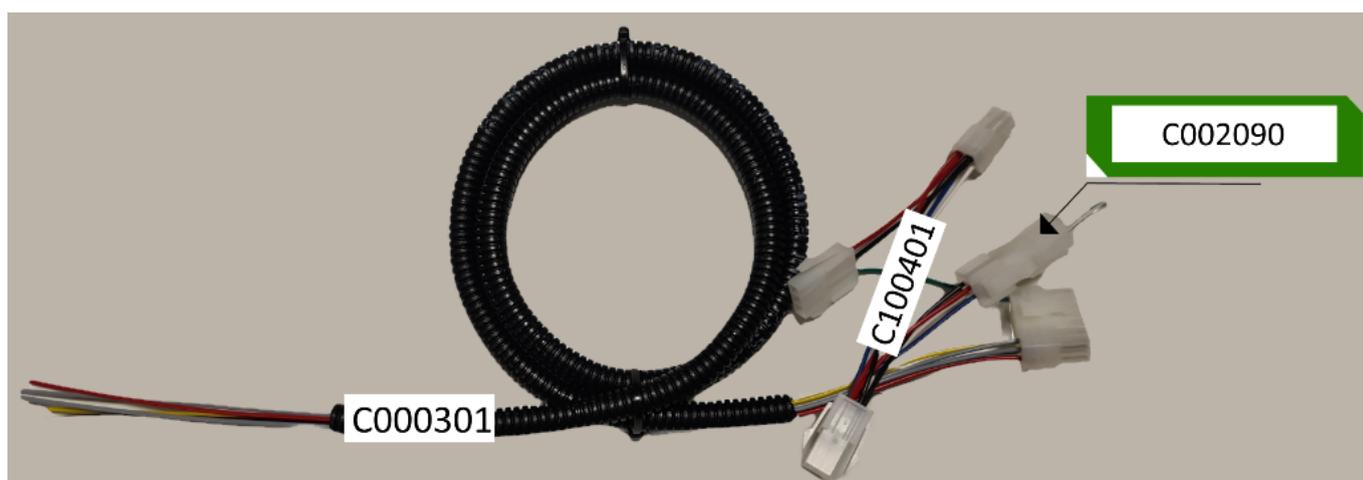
Cable KeyDN - Máquina: C000301 + C100401 + C002090
